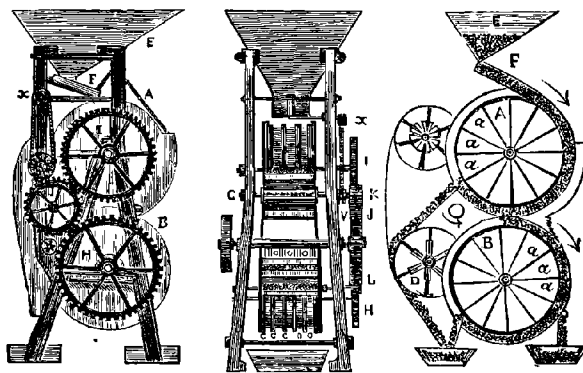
TRIEUR MAGNÉTO-MÉCANIQUE.
